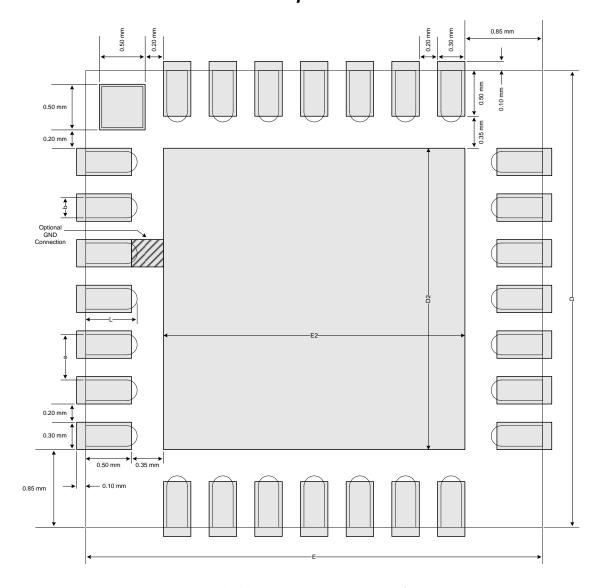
典型的 C8051F327 QFN-28 焊盘图
